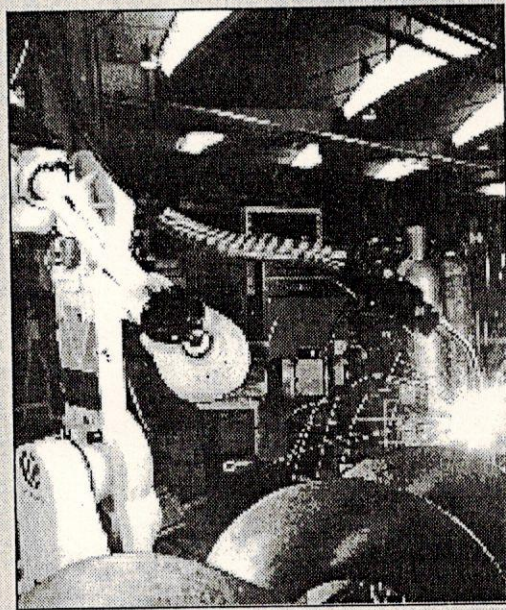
Robot de soldadura (Gentileza de Rubén Constantini S.A.)
